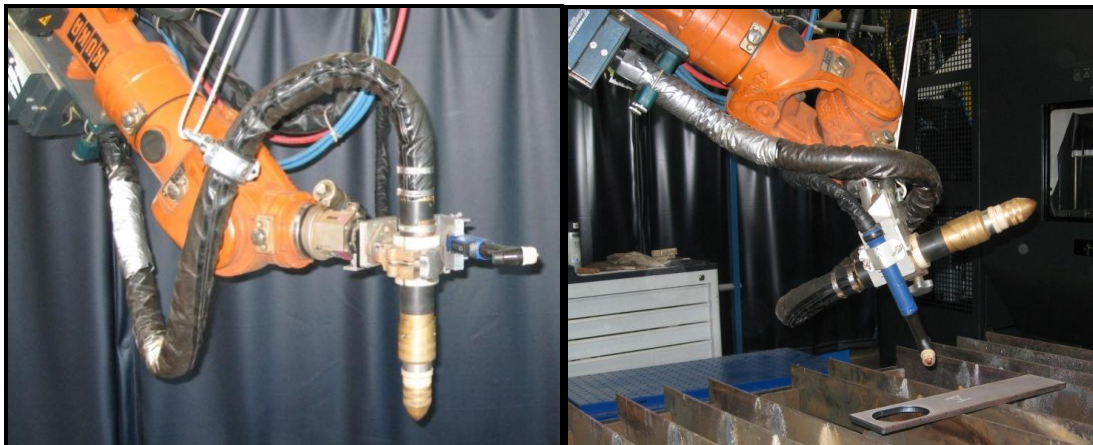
Plasmabrenner mit versetztem Werkzeug zum thermischen Kantenbearbeiten
